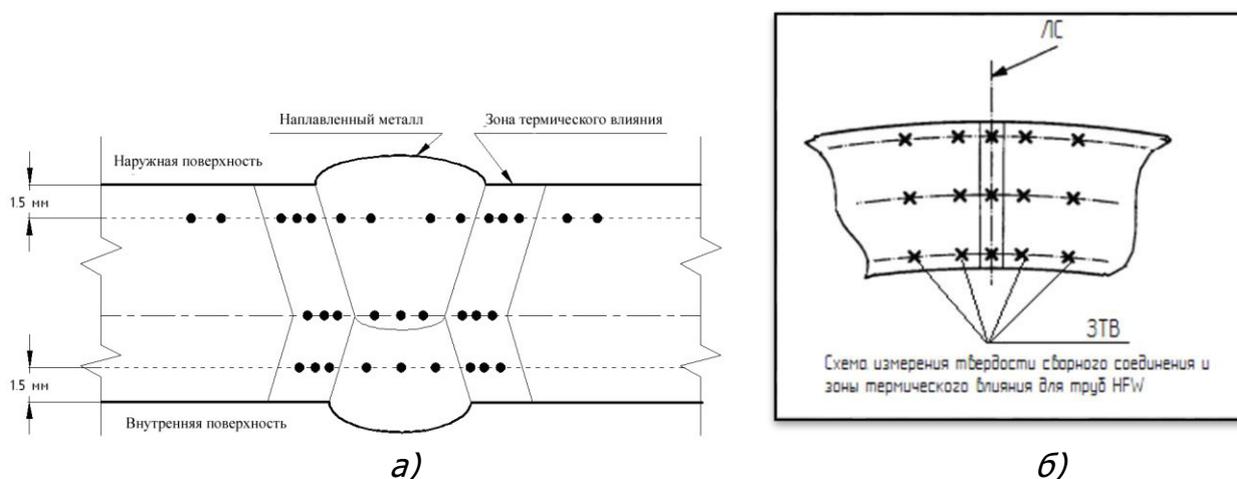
Схема измерения твердости сварного соединения:
